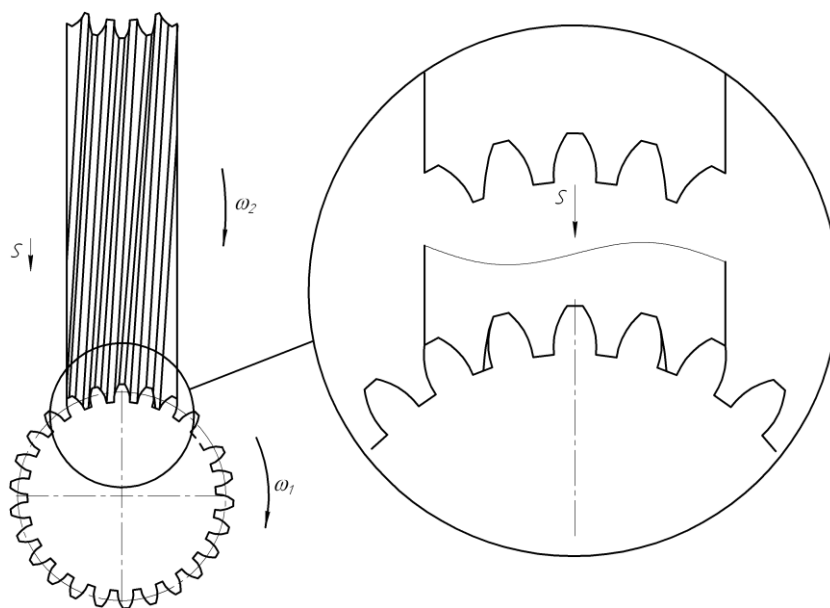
Врезное шлифование цилиндрического зубчатого колеса глобоидным червячным шлифовальным кругом [108]
